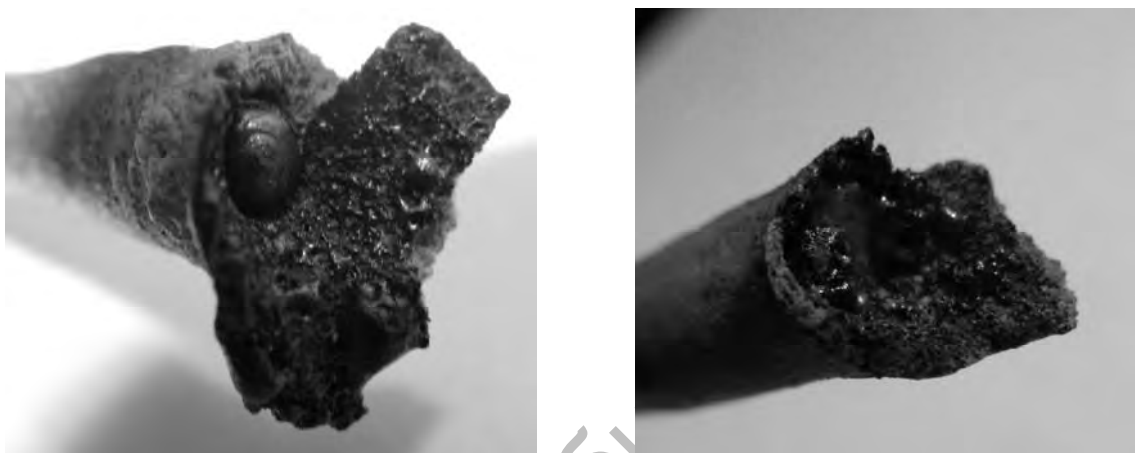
Внешний вид оплавленной части сварочного электрода
